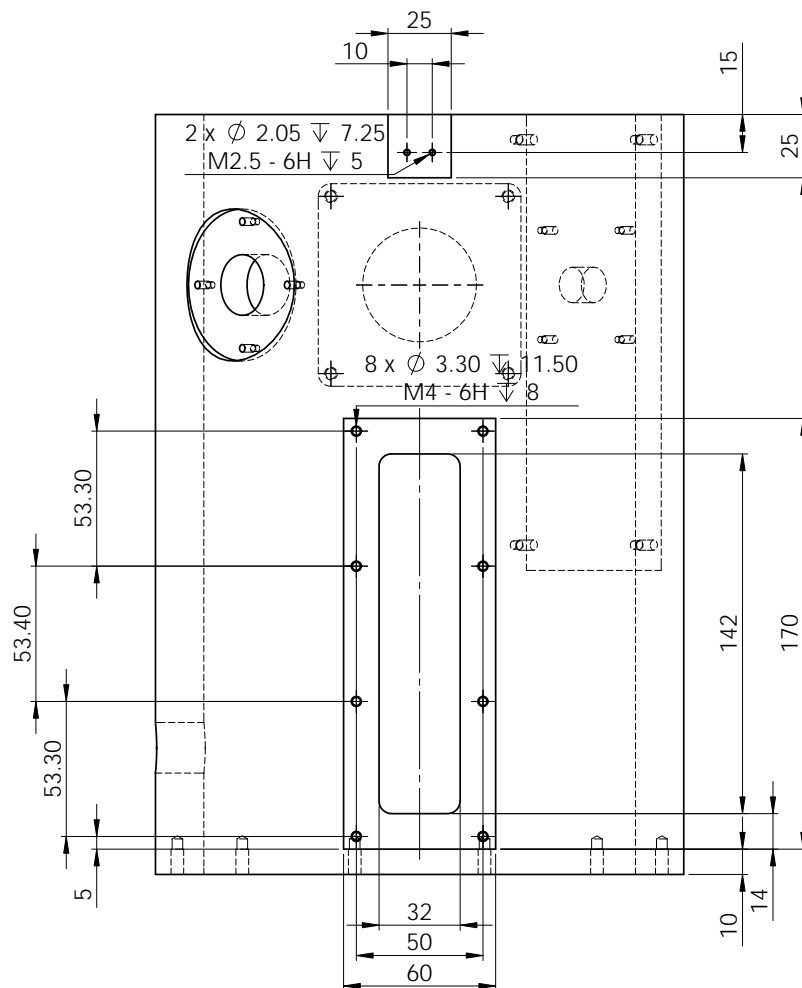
Technische Zeichnung der Vakuumröhre auf der Steckerflanschseite.
